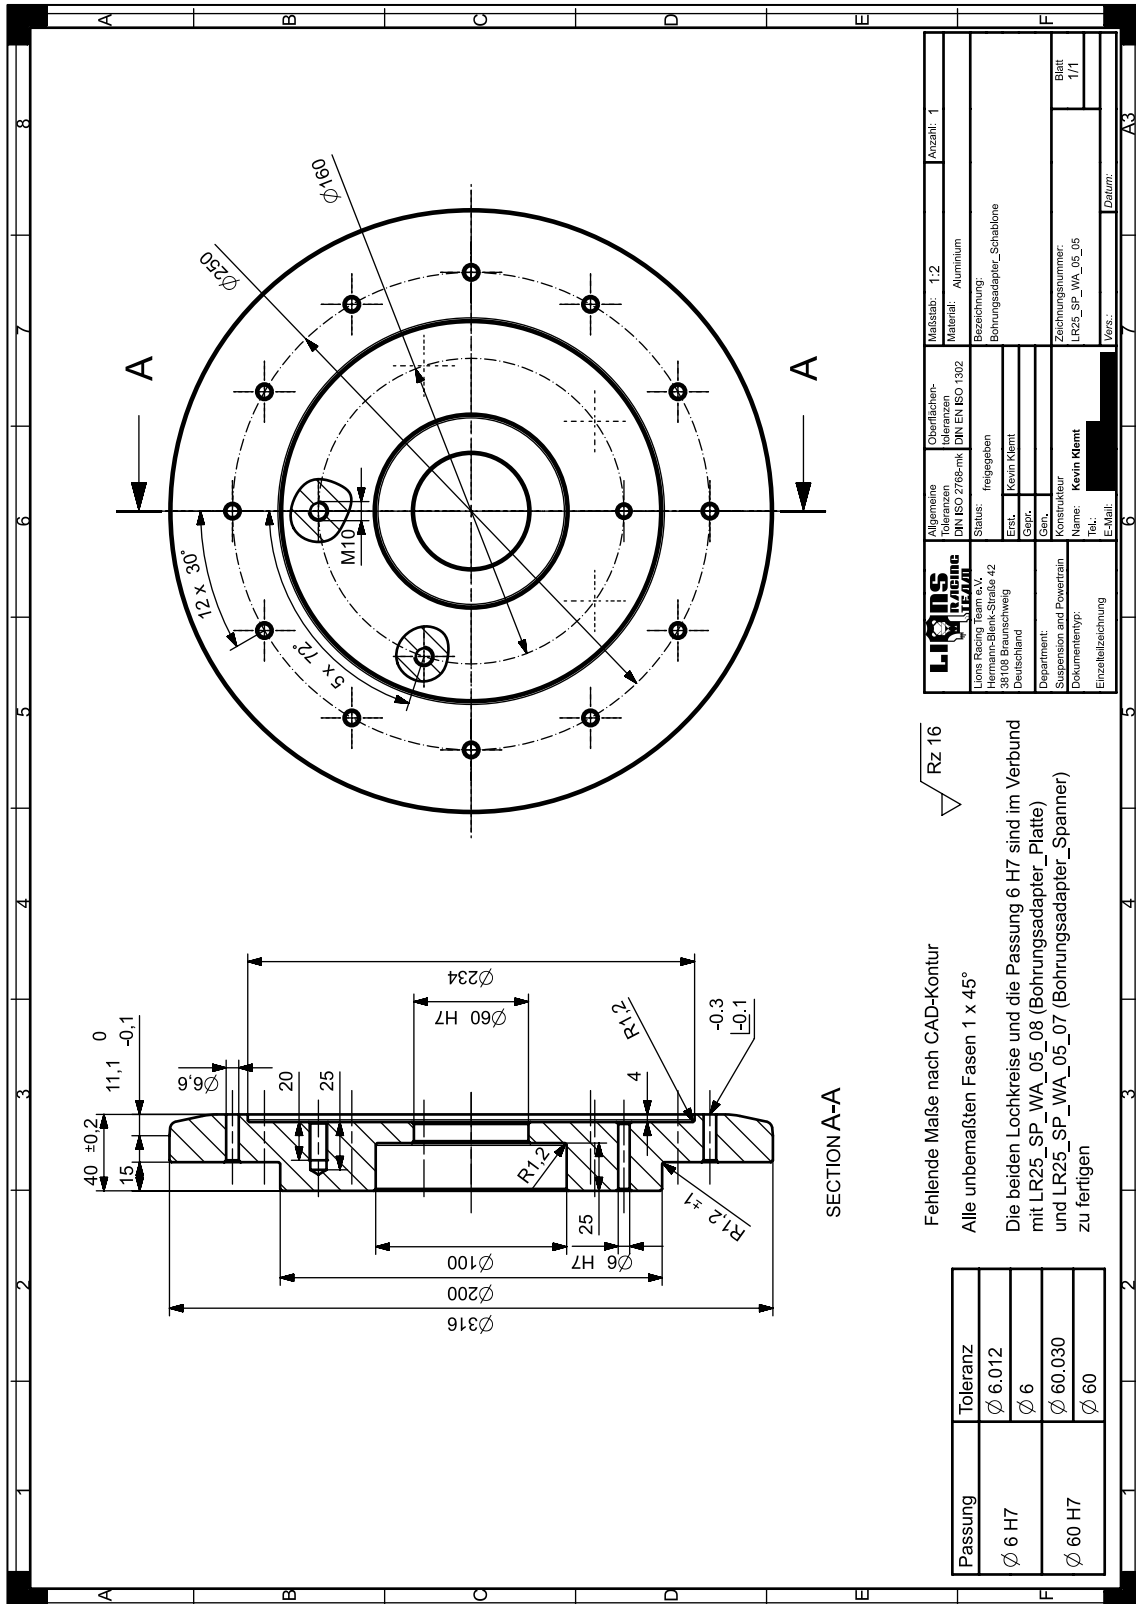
Technische Zeichnung Bohradapter (1/4); Schablone [42]
